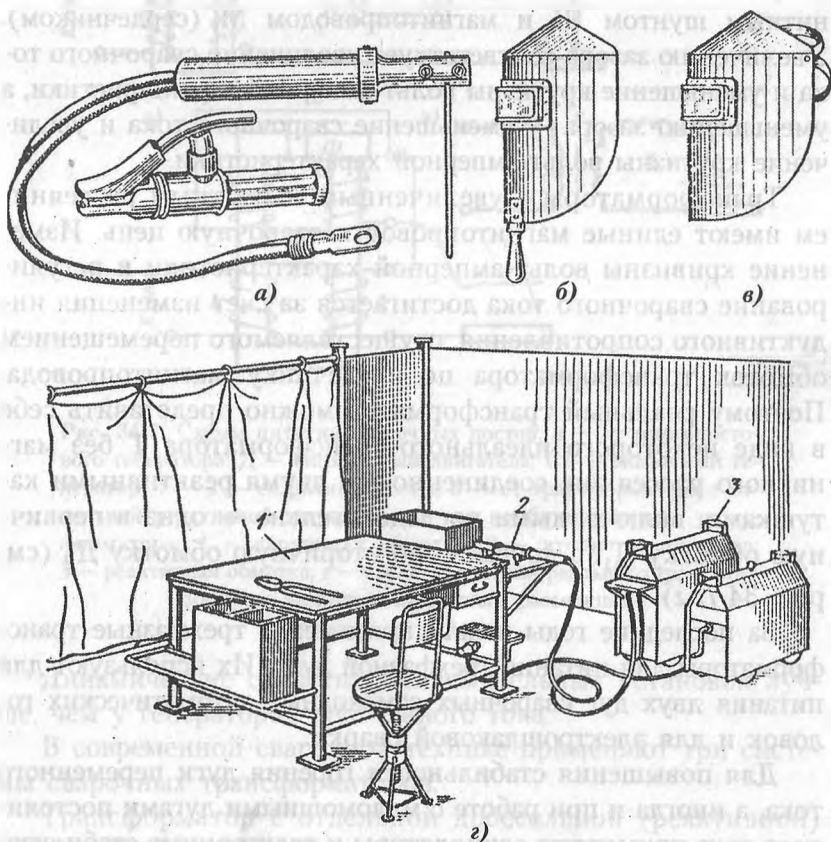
Электрододержатели (а), предохранительный щиток (б), маска (в) и рабочее место для ручной дуговой сварки (г): 1 — стол; 2 — электрододержатель; 3 — сварочный трансформатор
